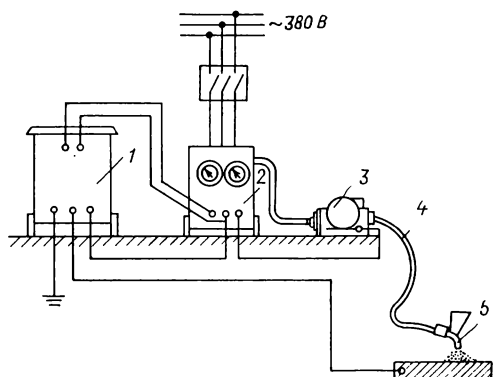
Схема установки для полуавтоматической сварки под флюсом.
